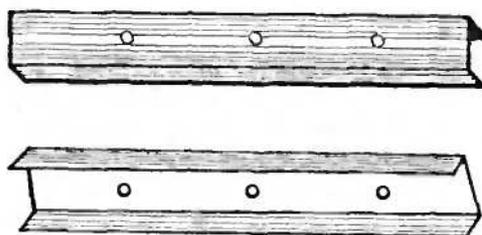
Шаблон для разметки и прокола отверстий в боковых планках рамок
